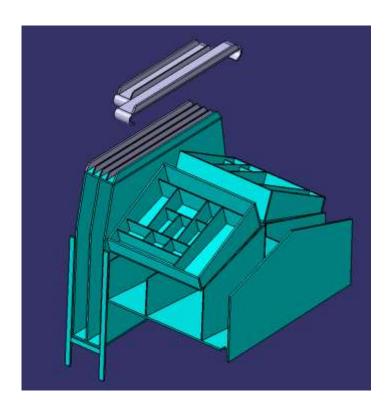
3D модель комплекта пластиковых ящиков из полипропилена для транспортировки деталей
